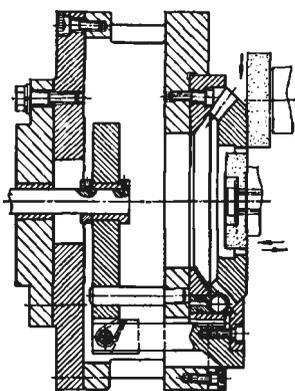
Схема шлифования отверстия и торца чашечным кругом
